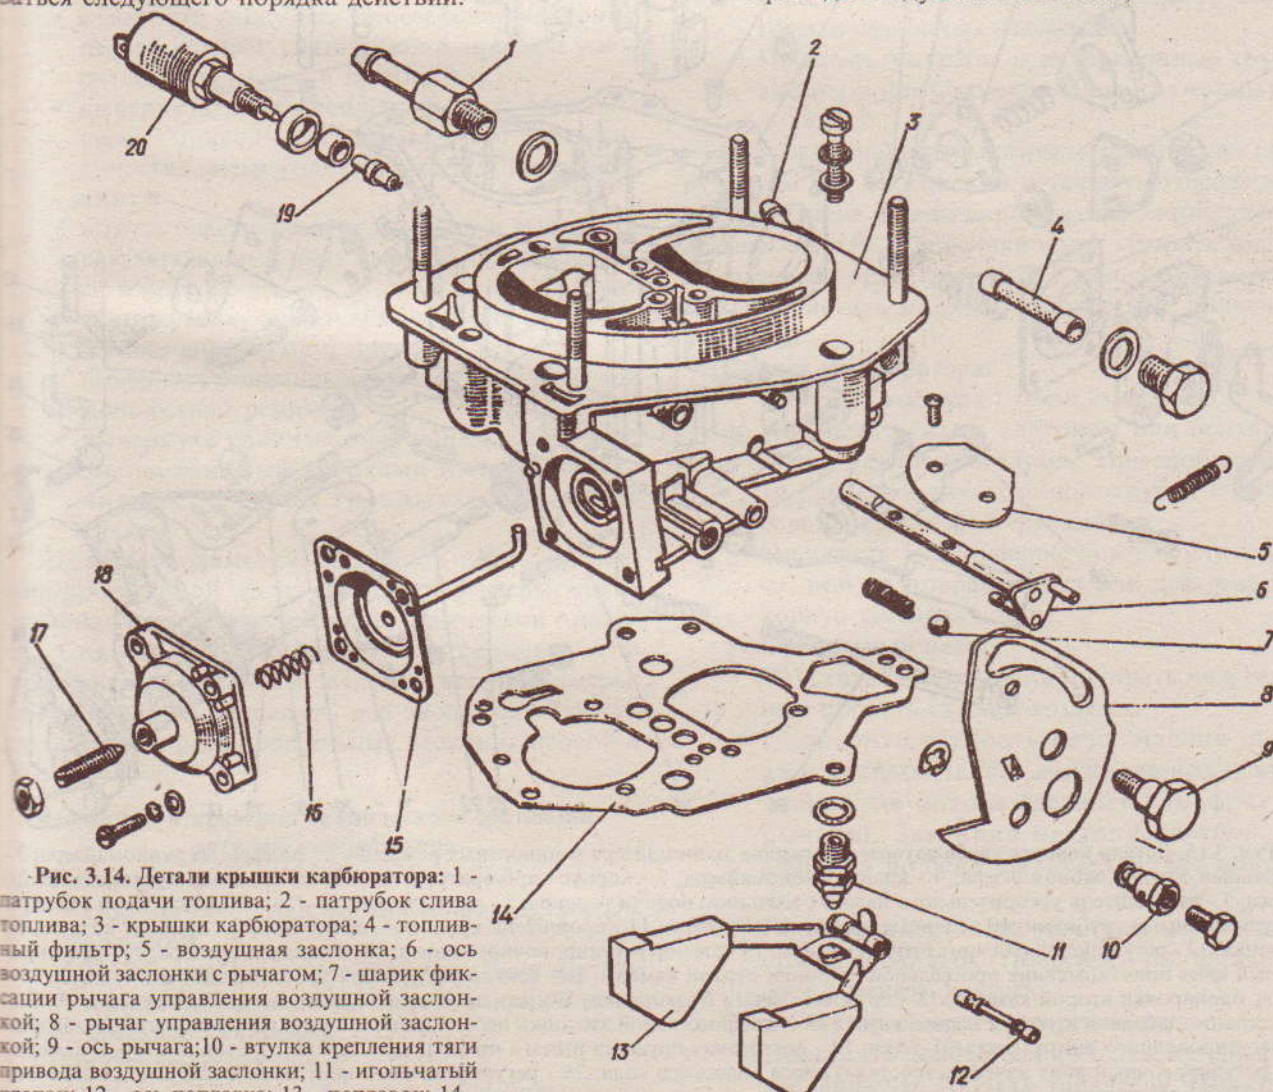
Детали крышки карбюратора: 1 - патрубок подачи топлива; 2 - патрубок слива топлива; 3 - крышки карбюратора; 4 - топливный фильтр; 5 - воздушная заслонка; 6 - ось воздушной заслонки с рычагом; 7 - шарик фиксации рычага управления воздушной заслонкой; 8 - рычаг управления воздушной заслонкой; 9 - ось рычага; 10 - втулка крепления тяги привода воздушной заслонки; 11 - игольчатый клапан; 12 - ось поплавка; 13 - поплавок; 14 - прокладка; 15 - диафрагма пускового устройства со штоком; 16 - пружина; 17 - регулировочный винт; 18 - крышка пускового устройства; 19 - топливный жиклёр холостого хода; 20 - электромагнитный запорный клапан
